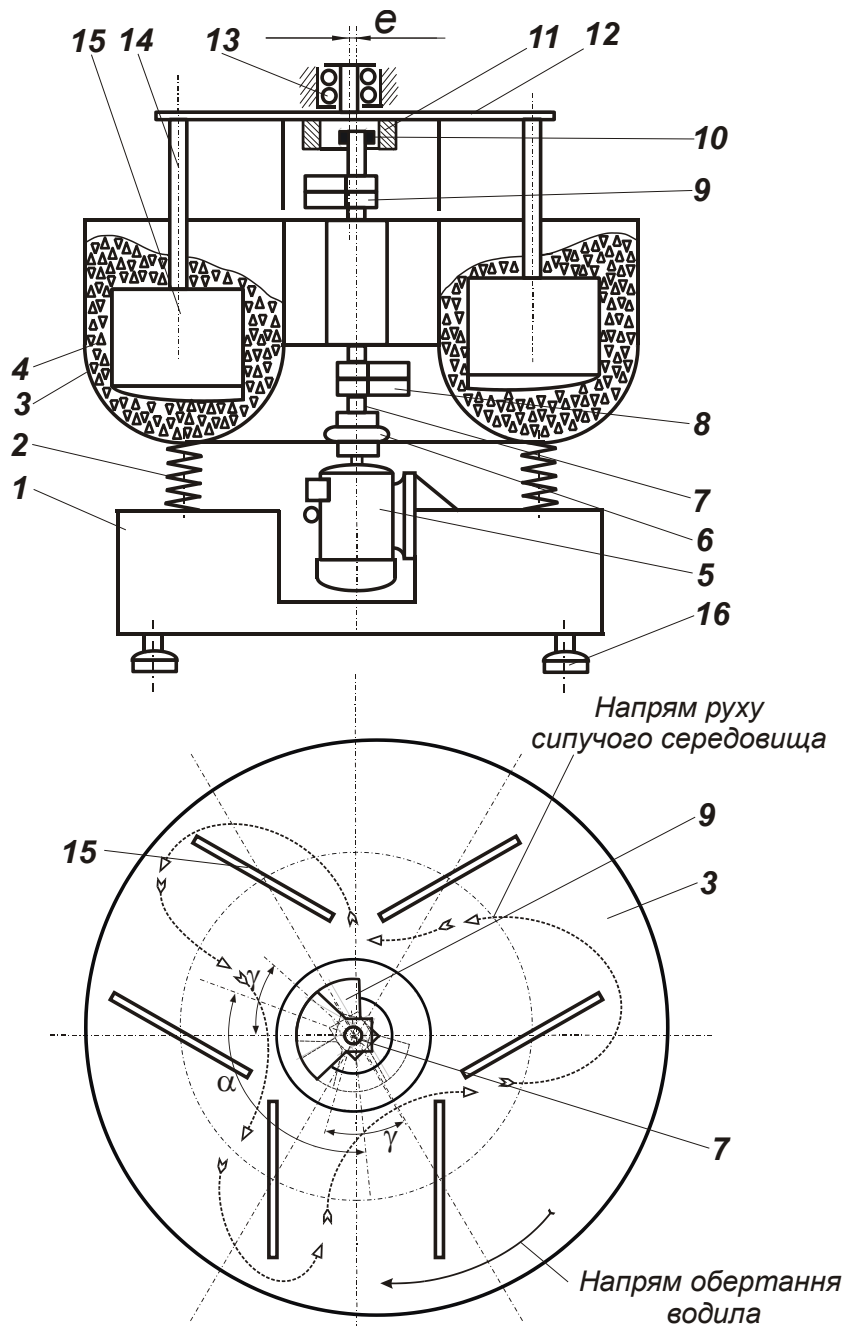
Конструктивна схема вібраційного змішувача з вертикальними привідним та лопатевим валами:
